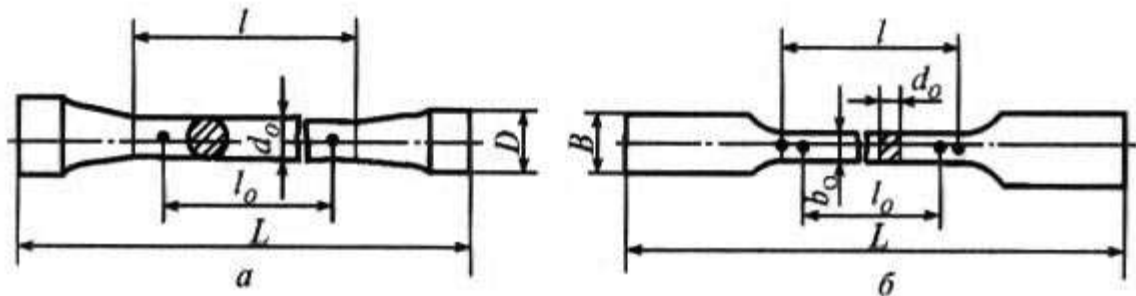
Загальний вигляд стандартних зразків для випробувань на розтяг: а - циліндричний зразок; б — плоский зразок.
